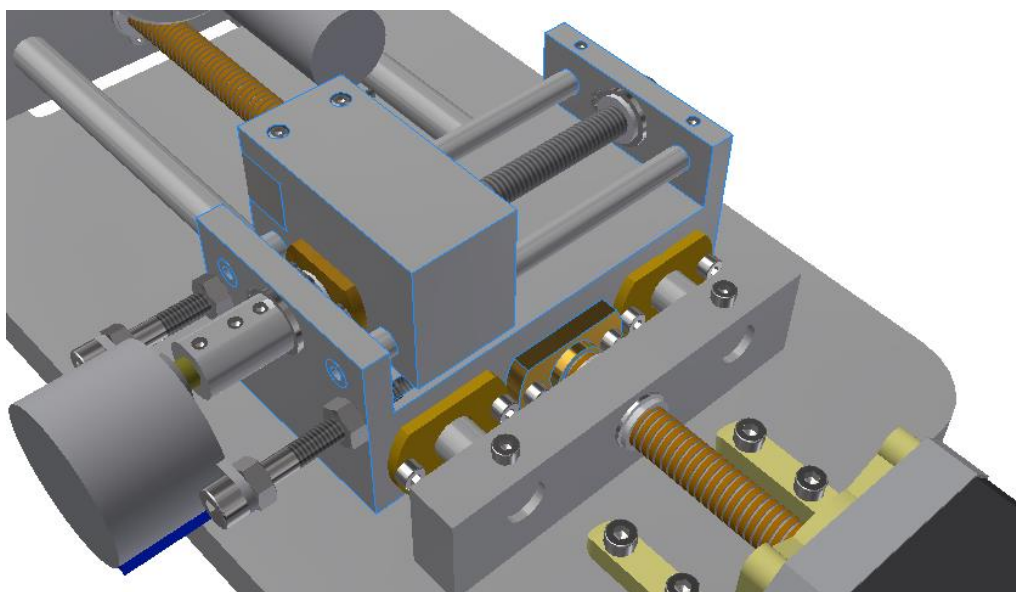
detalhe do conjunto do carro transversal e longitudinal em CAD
